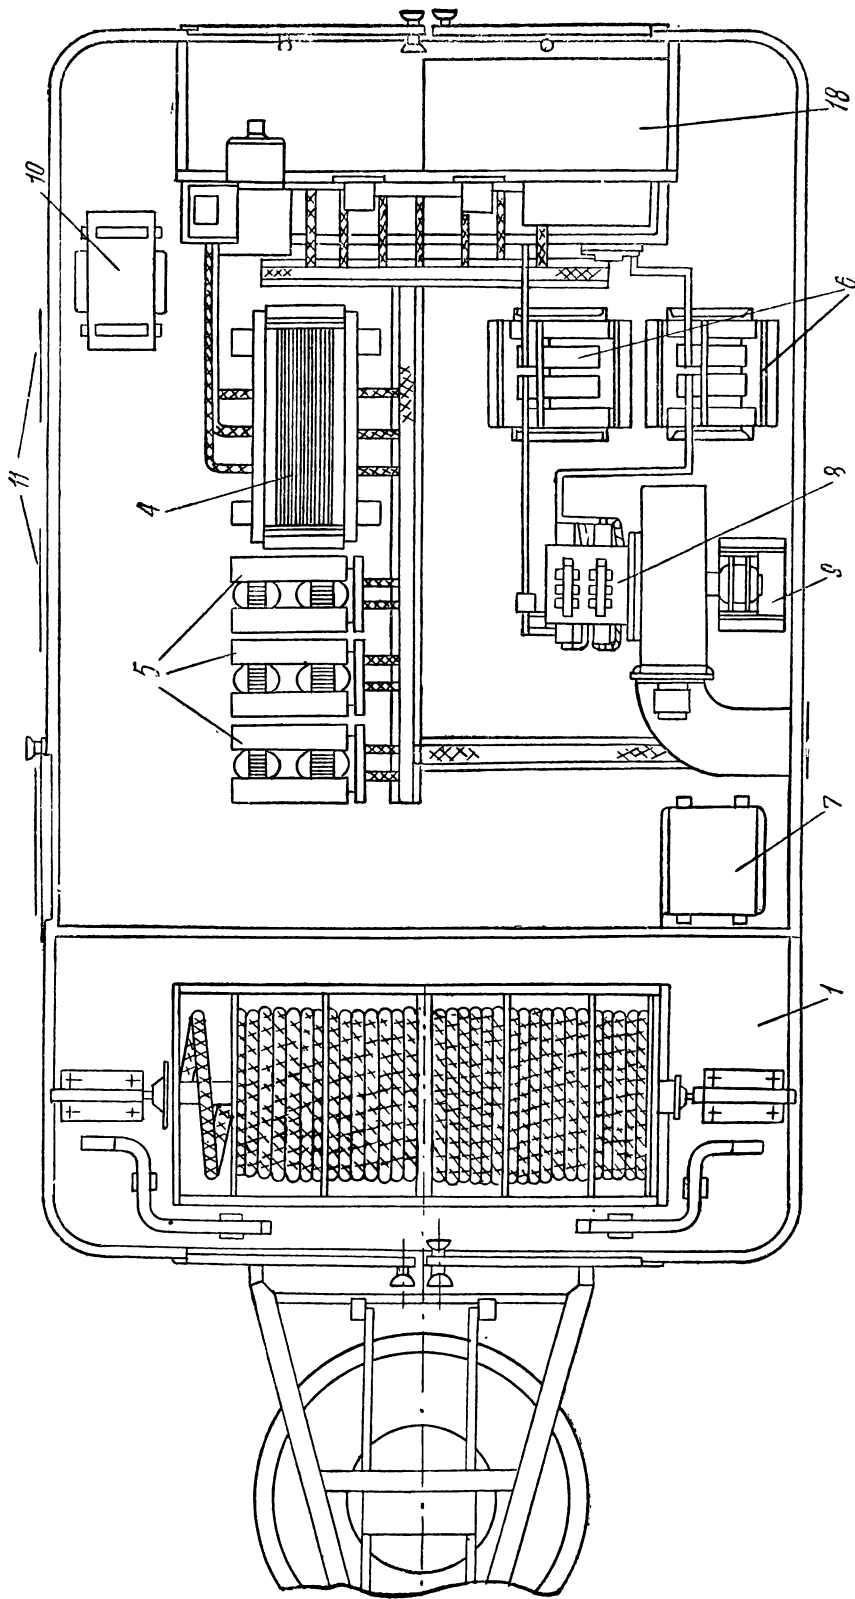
Компоновка оборудования кремниевого передвжного выпрямителя ВКП-600 (вид сверху)
